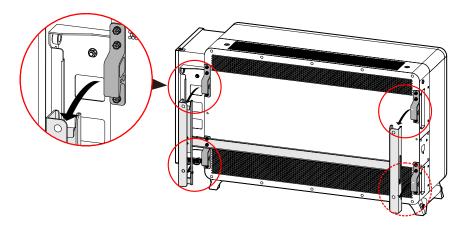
Montaggio dell'inverter sul supporto di installazione
